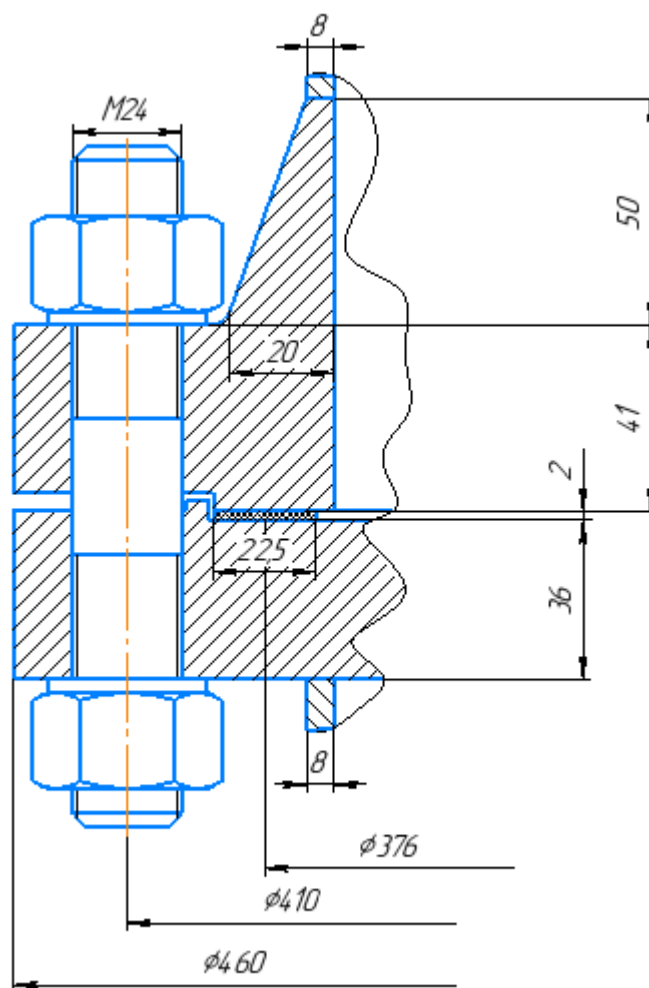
Фланцевое соединение с приварными встык фланцами с уплотнительной поверхностью типа выступ-впадина [23]
